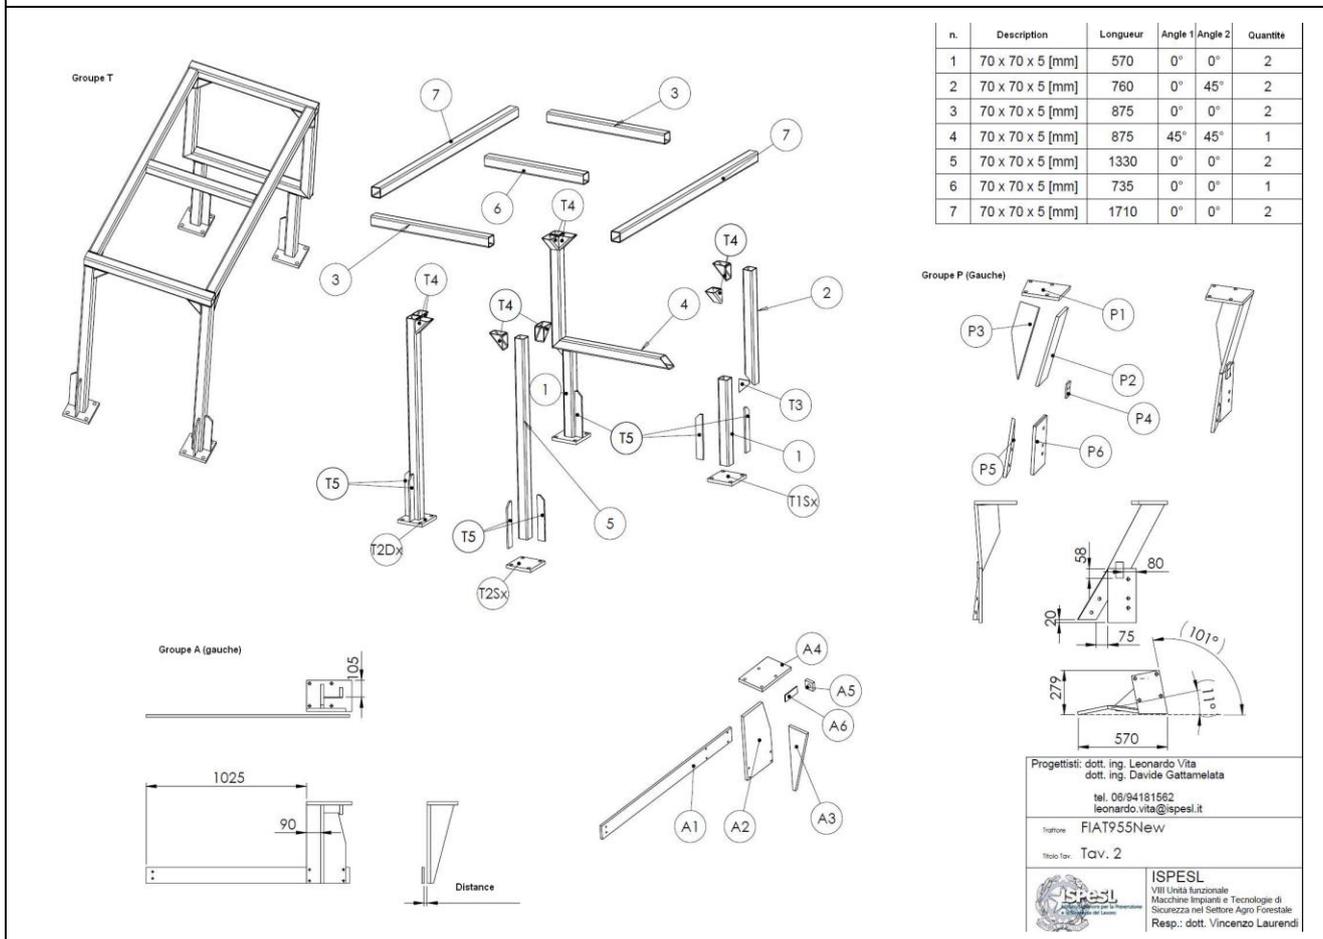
Structure de protection pour tracteur à chenilles de type FIAT 955
